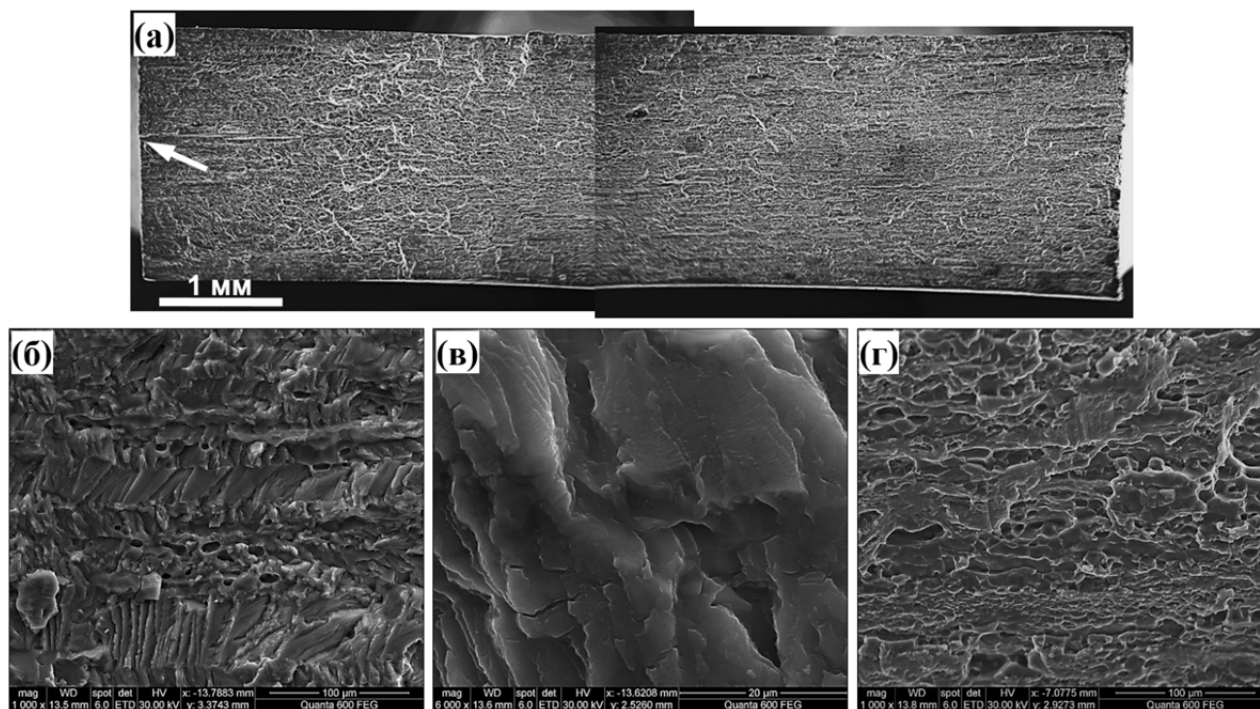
Типичная поверхность разрушения усталостного образца, вырезанного из сварного шва: (а) общий вид, (б) область зарождения трещины, (в) область стабильного распространения трещины и (г) область катастрофического разрушения. На рис. (а) стрелкой указано место вероятного зарождения трещины.
